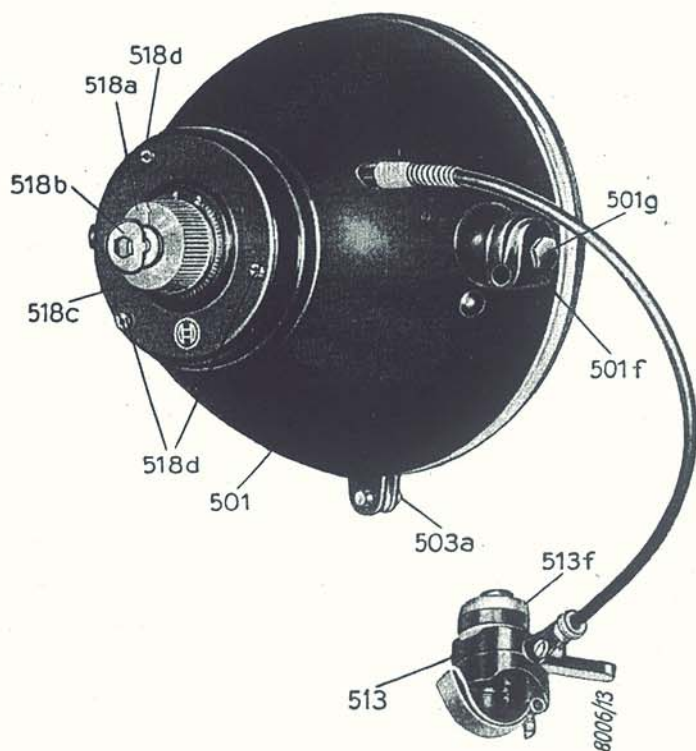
Scheinwerfer für seitliche Befestigung (Rückansicht)
